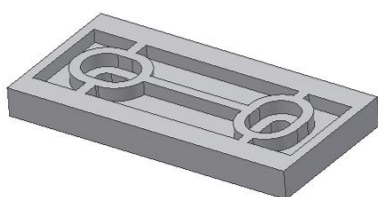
Otvory pro vrty – přední strana technického dílu.
